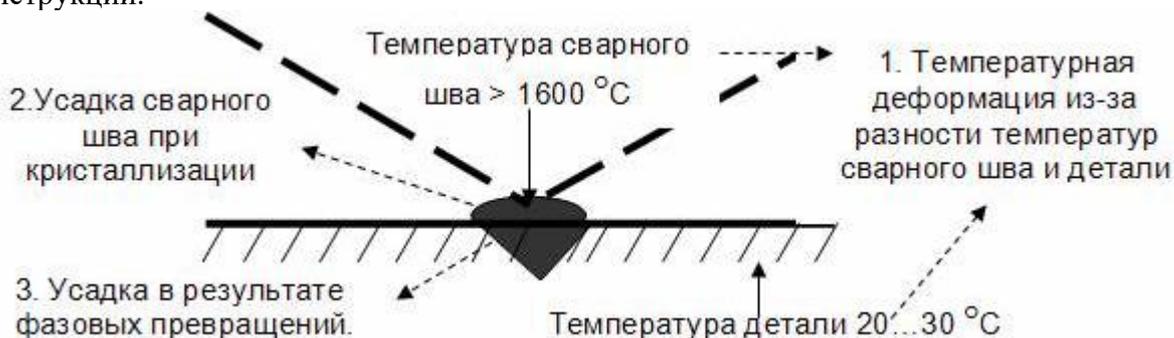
Причины деформаций деталей при сварке
